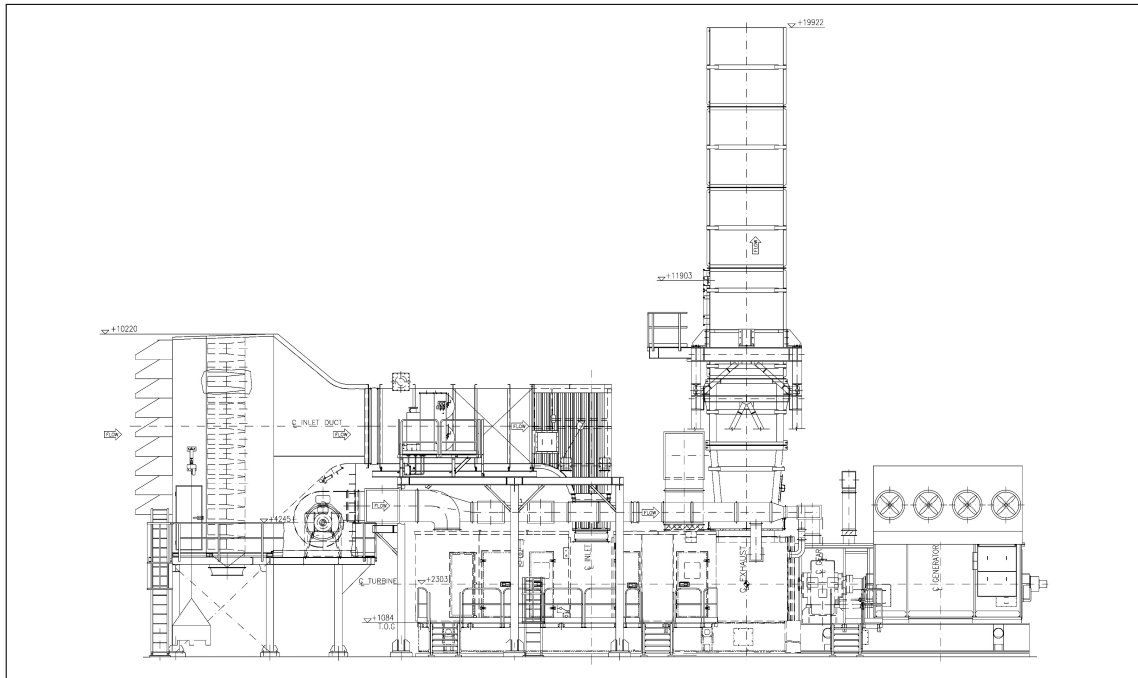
Plan d'implantation du turboalternateur (SOM6622814)[17]
